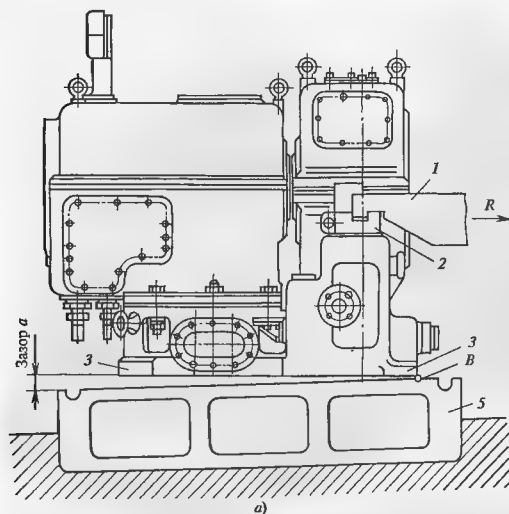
Крепление корпуса подшипника к фундаментной раме
